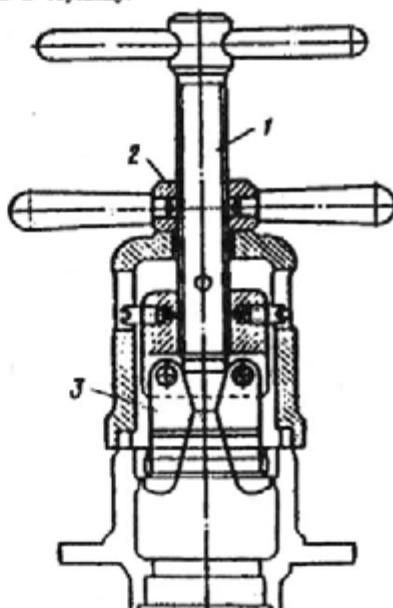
Съемник для выпрессовки наружных колец подшипников из ступицы колес:
